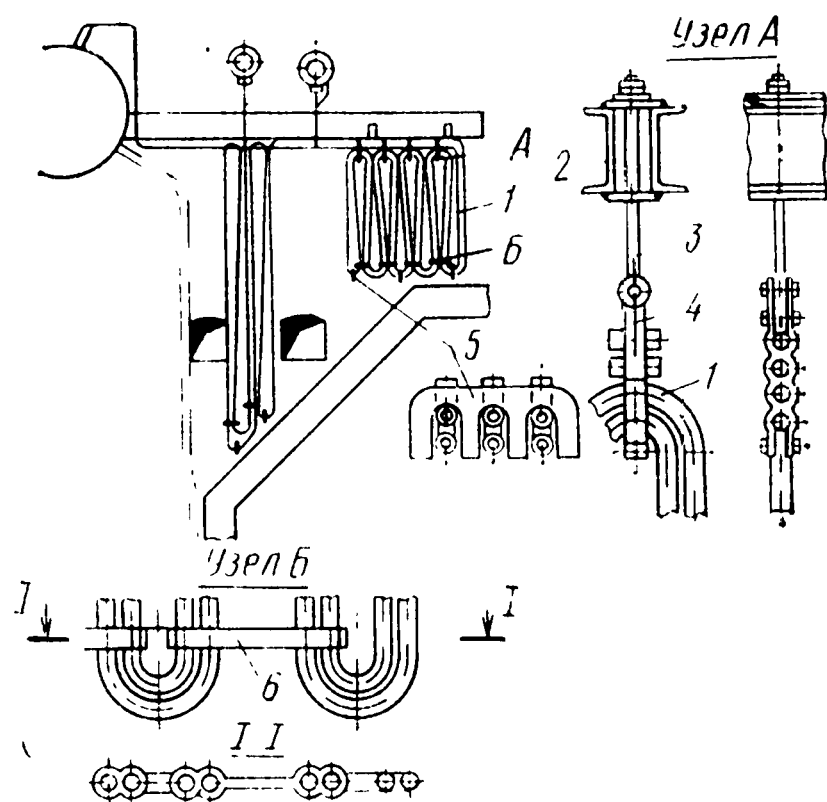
Конструкция крепления змеевиков пароперегревателя
